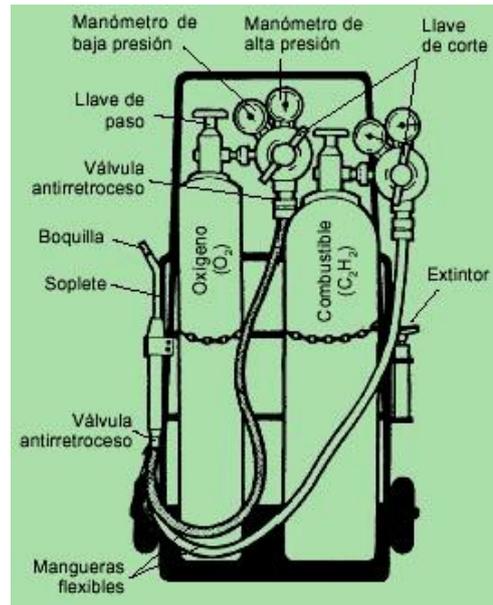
Elementos principales de una instalación móvil de soldadura por gas
